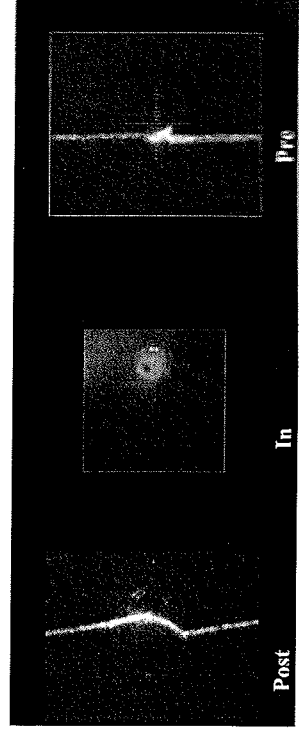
Schweißen von Aluminium (Messung S02.5, Bild Nr. 6)
